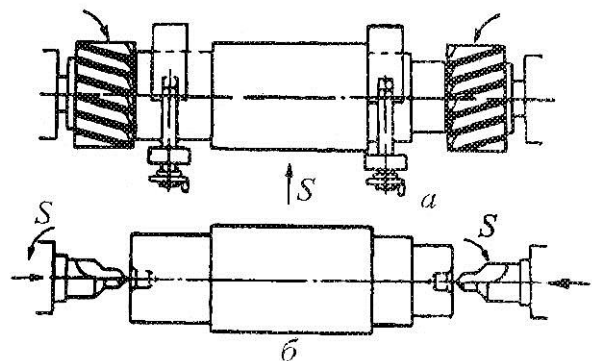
Схеми обробки торців валів на фрезерно-центрувальних верстатах
